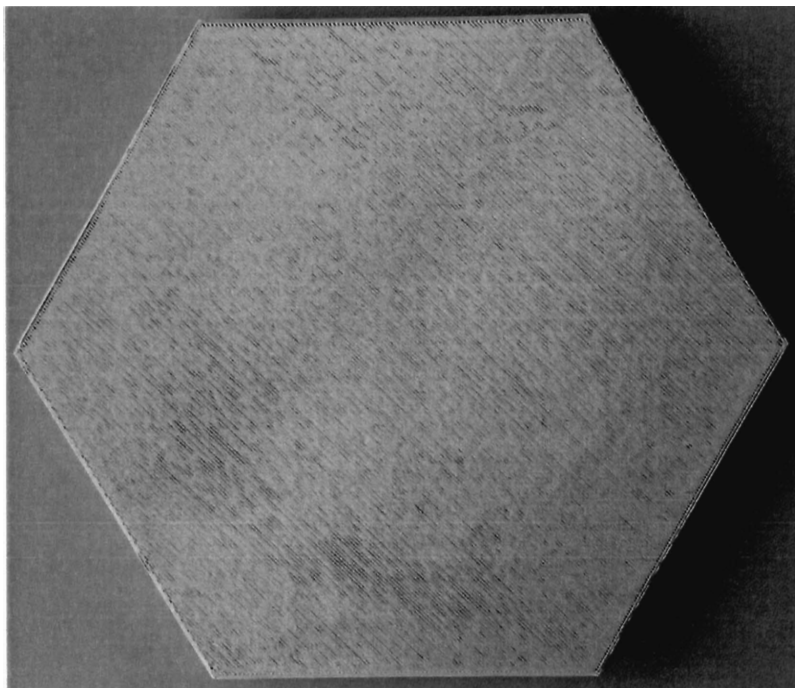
Vedere frontală platoșă protecție hexagon – TIP 2
